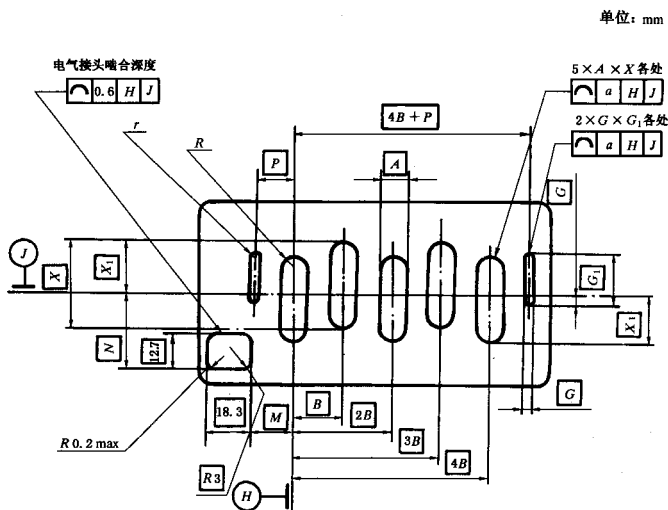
规格 1E、2E、3E 安装面的外形尺寸和公差
